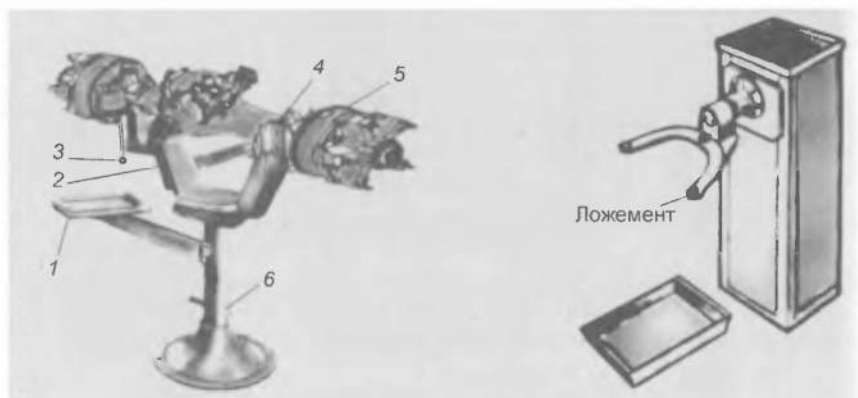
Стенд для разборки и сборки мостов автомобиля: 1 — подставка для сборочных единиц; 2 — ложемент; 3 — рукоятка крепления моста; 4 — фиксатор; 5 — мост автомобиля; 6 — стойка
